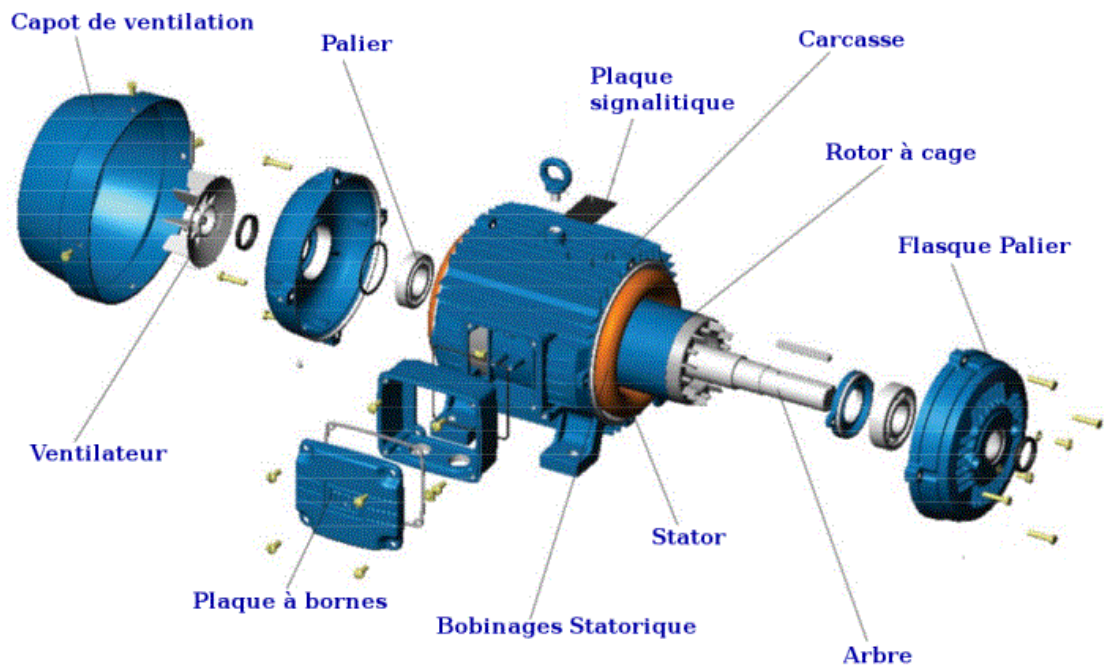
Vue éclatée du moteur asynchrone à cage
